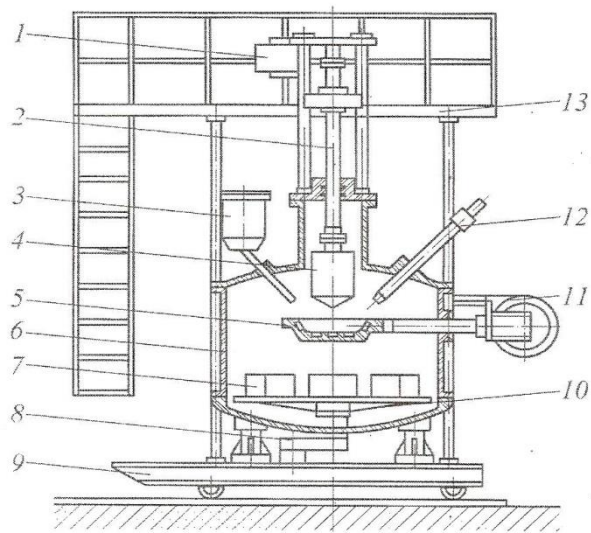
Плазмово-дугова гарнісажна ливарна установка УП-109
